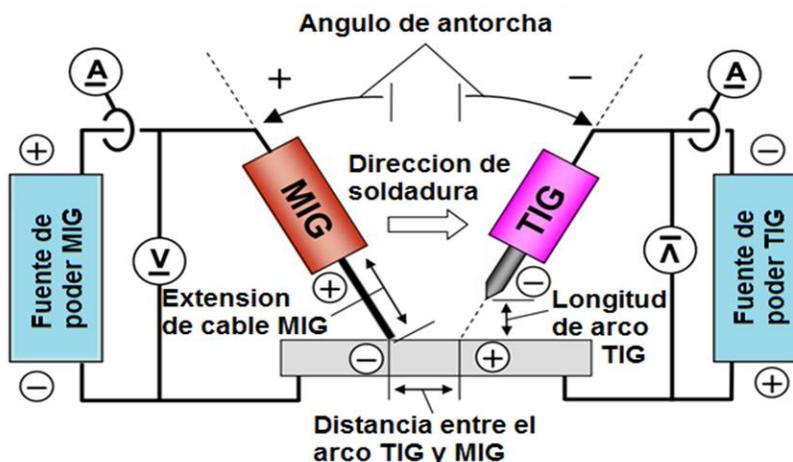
Esquema del proceso de soldadura híbrido GTAW-GMAW. Modificado de Kanemaru, Shuhei, et al (2014)
